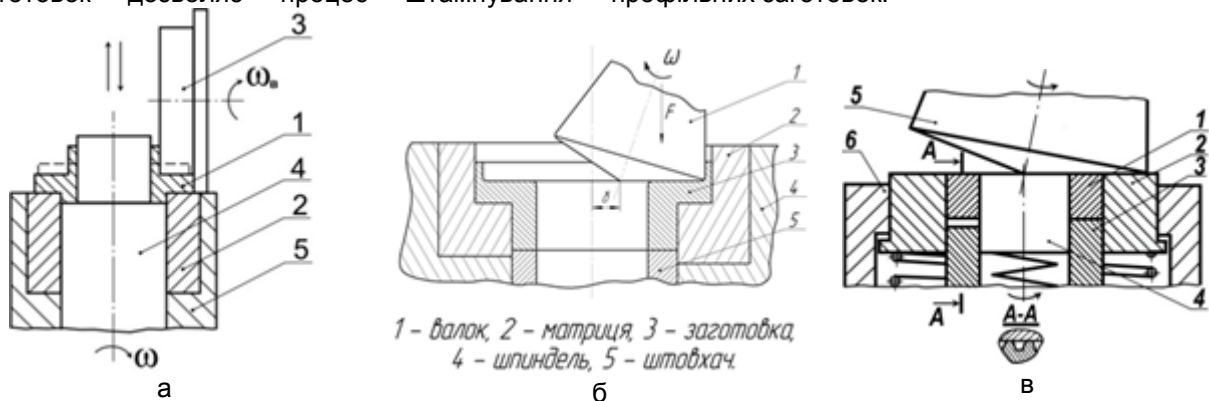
Схеми штампування обкочуванням кільцевої заготовки циліндричним і конічним валками
